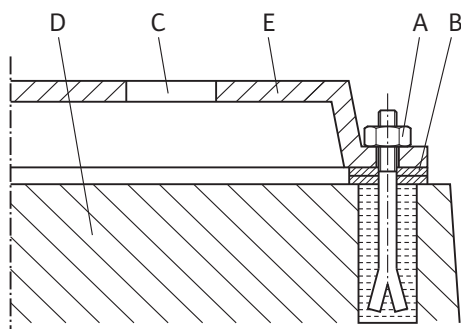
Voorbeeld voor een fundament-draadaansluiting
